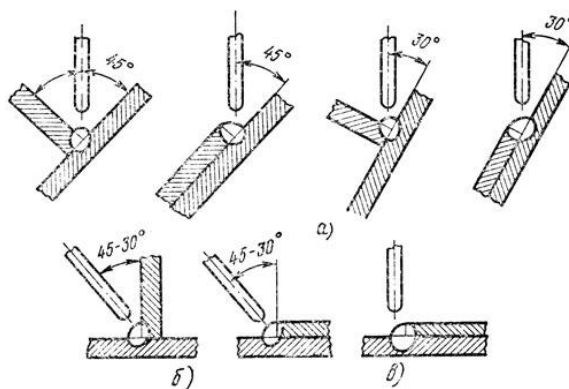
Способы выполнения угловых, тавровых и нахлесточных швов: а - сварка в симметричную и несимметричную 'лодочку', б - наклонным электродом, в - сварка с оплавлением кромки
